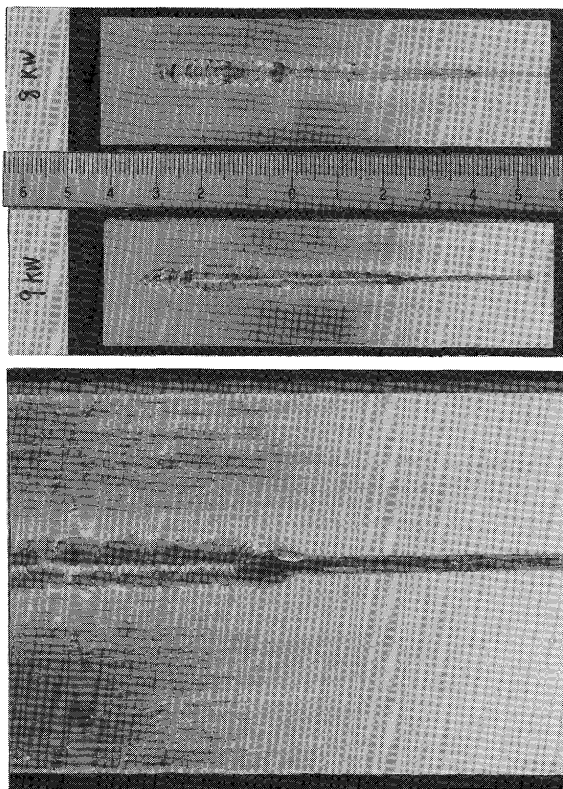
Schweissraupen-Erscheinung und Strahl-Spur auf reinem Aluminium
